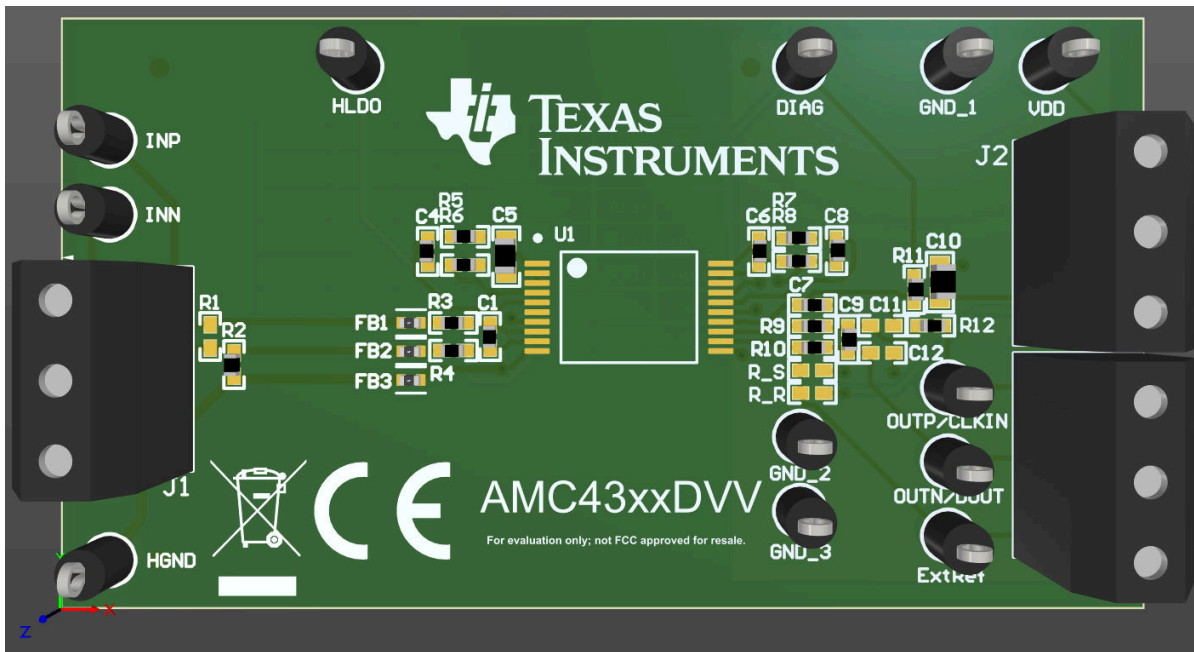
AMC43xxDVVEVM 顶部 3D PCB 图
